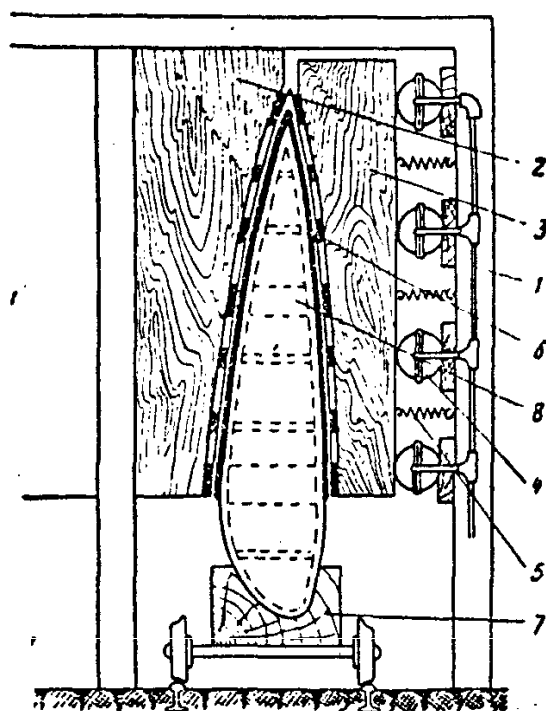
Пневматический пресс для установки плоскостной обшивки на каркас консоли.
